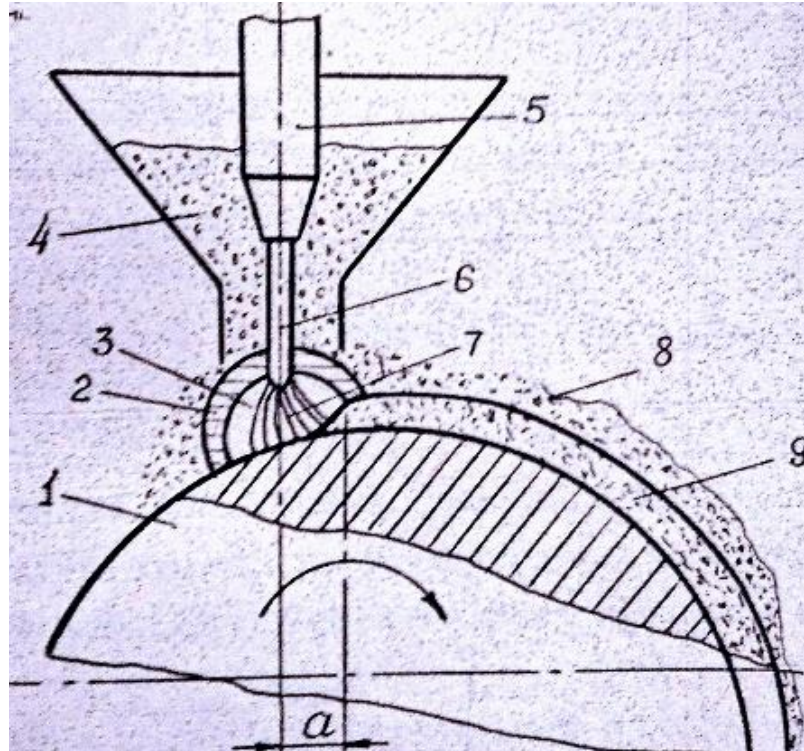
Схема автоматичної наплавки: 1 – наплавлювана деталь; 2 – оболонка рідкого флюсу; 3 – еластична оболонка; 4 – бункер із флюсом; 5 – мундштук; 6 – електрод; 7 – електродуга; 8 – шлакова кірка; 9 – наплавлений метал
